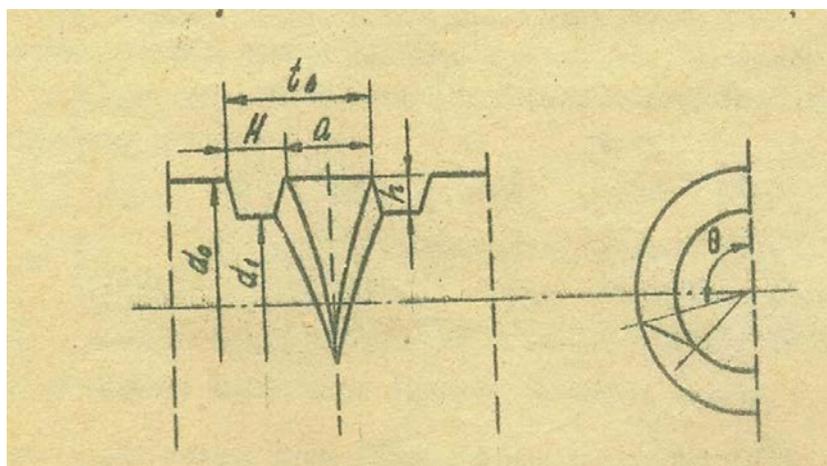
Профиль резьбы ходового винта канатоукладчика
